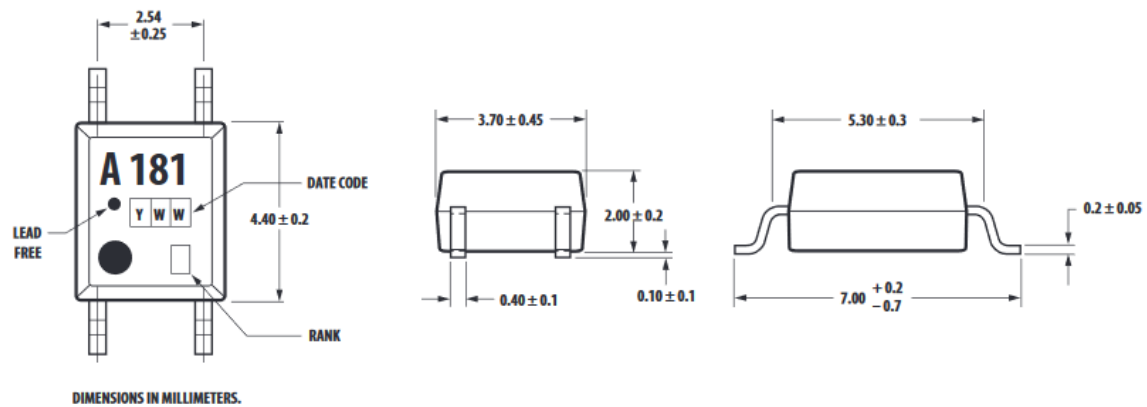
HCPL-181-00BE dimensiones y forma del package.
